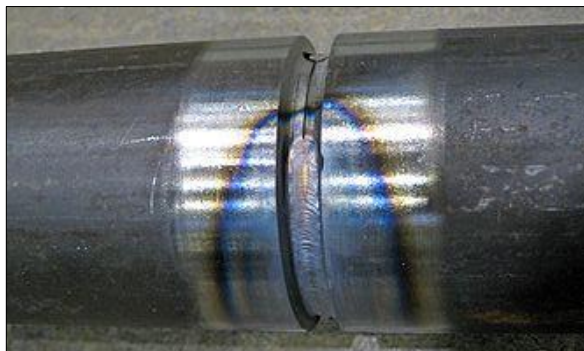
FOTOGRAFÍA DE LA ZONA AFETADA POR EL CALOR DE LA UNIÓN SOLDADA DE TUBERÍAS DE ACERO.
